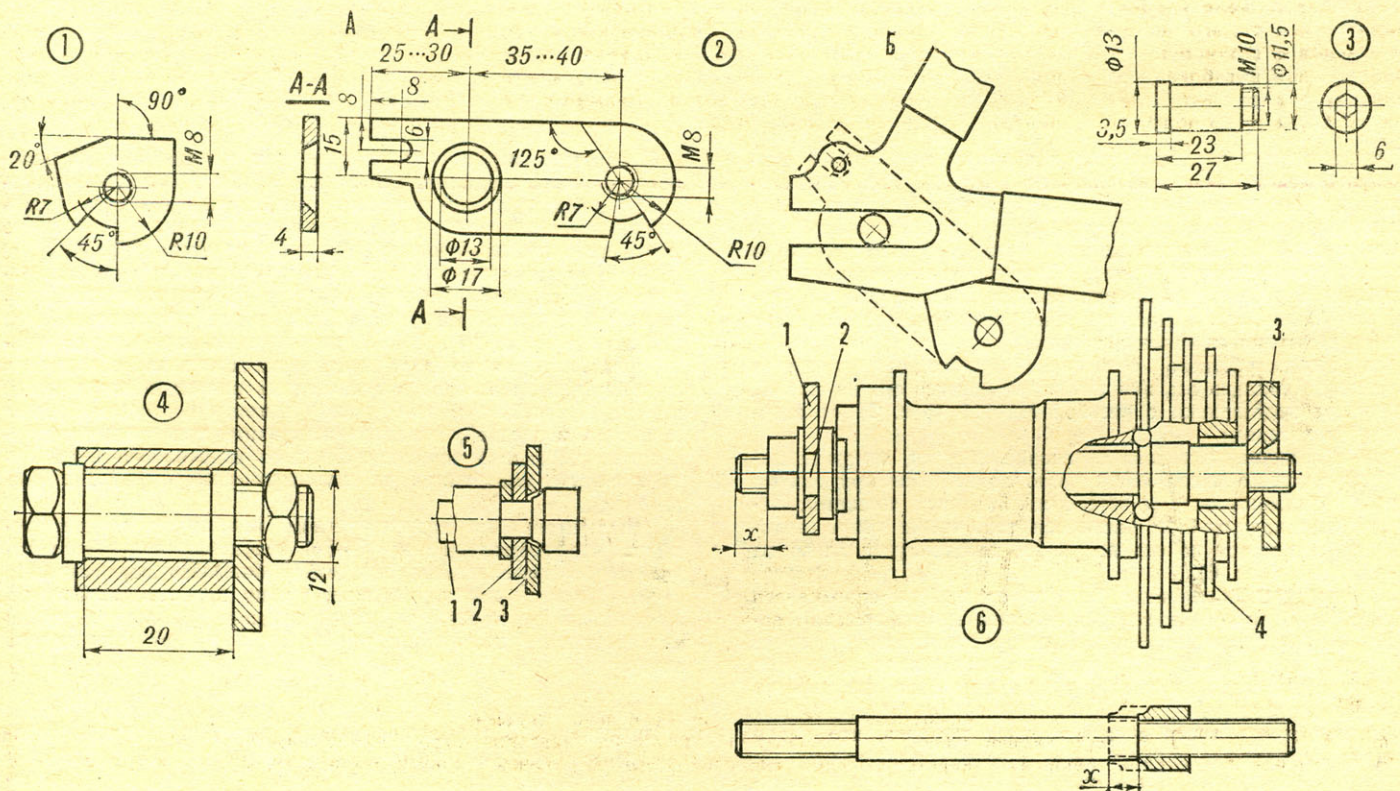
Пластина, устанавливаемая на болтах: А — развертка, Б — схема установки на перу задней вилки.
